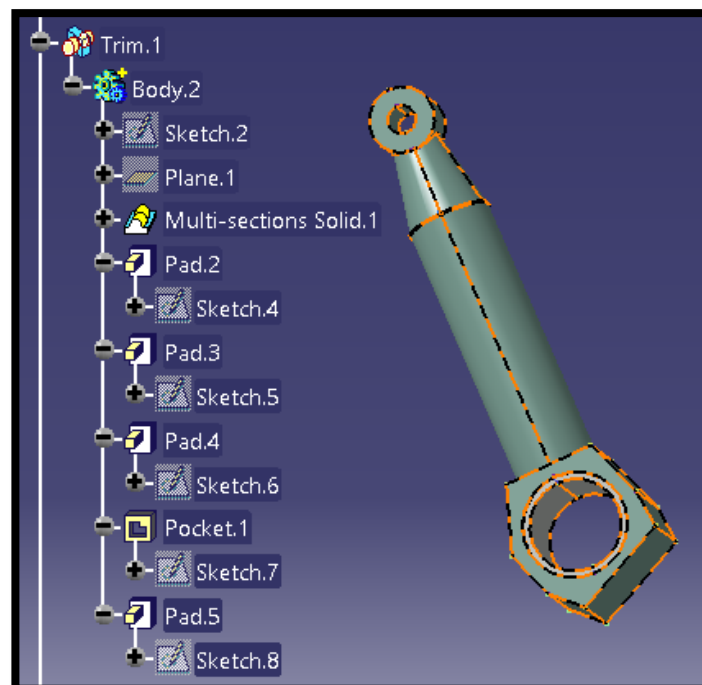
Seat mounting frame 11: Union trim brazo oscilante inferior
